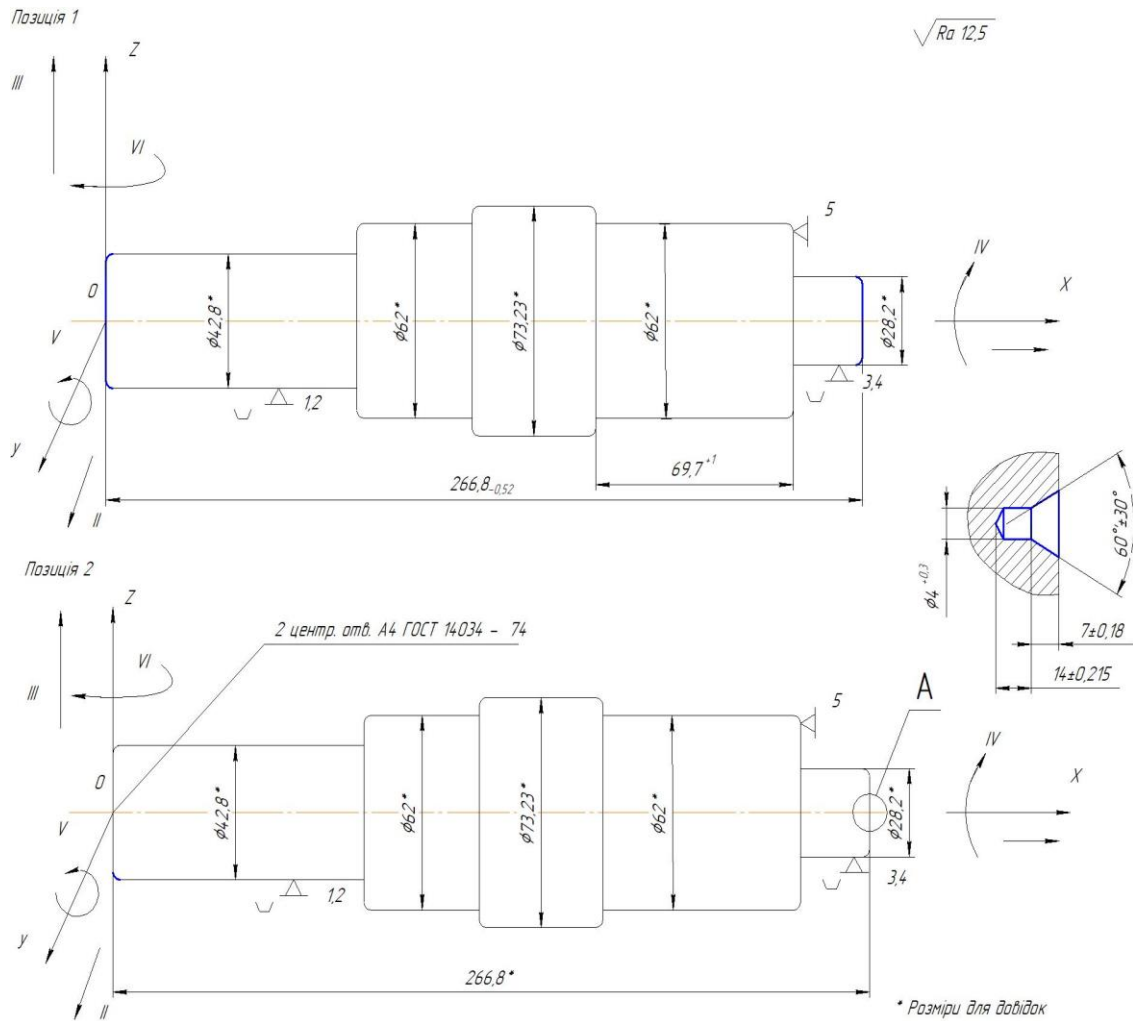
Схема базування на фрезерно-центрувальній операції
